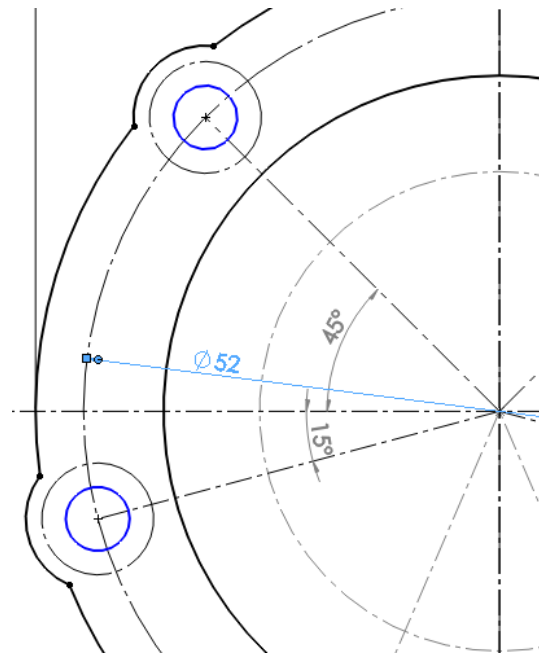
Posición de los agujeros de la pieza asiento rodamiento
